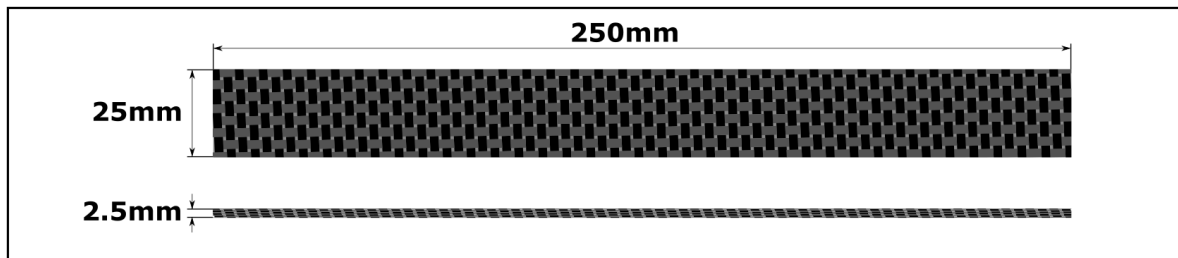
Dimensiones generales de probetas de material compuesto según ASTM D3039.
